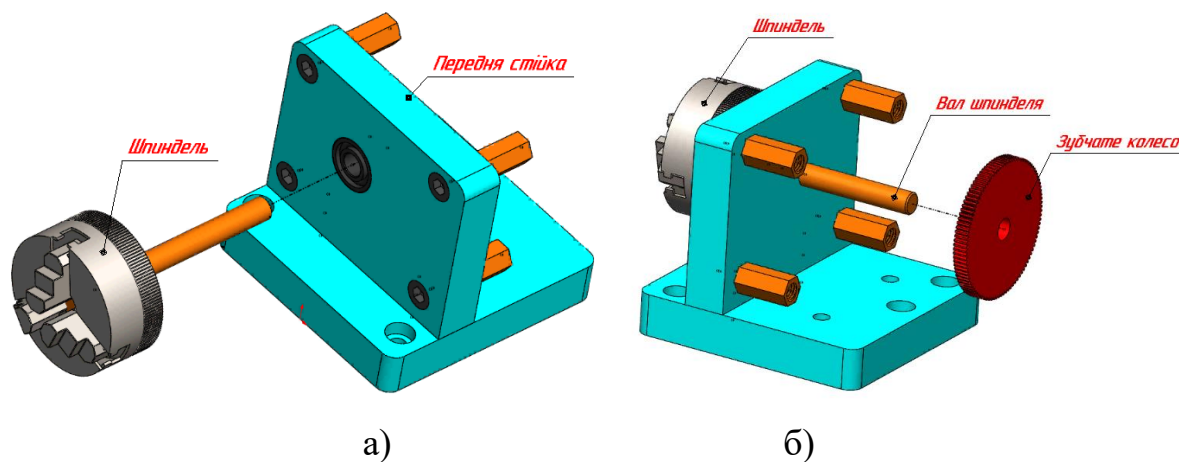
Монтаж шпинделя та зубчатого колеса
